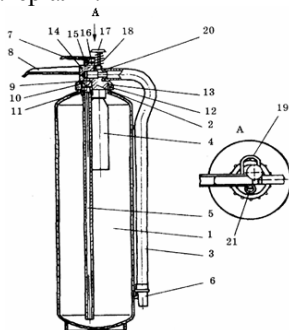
Вогнегасник порошковий ОП-9: 1 - корпус; 2 - головка; 3 - рукав; 4 - балон з робочим газом; 5 - трубка сифона; 6 - розпилювач; 7 - сітка; 8 - корпус фільтра; 9 - важіль керування клапаном; 10 - ручка; 11 - кільце ущільнювача; 12 - клапан; 13 - перехідник; 14 - гайка накидна; 15 - кільце ущільнювача; 16 - штифт; 17 - пружина; 18 - вісь; 19 - кнопка з голкою; 20 - пружина; 21 - запобіжна чека; 22 - кільце ущільнювача; 23 - запобіжний клапан.
